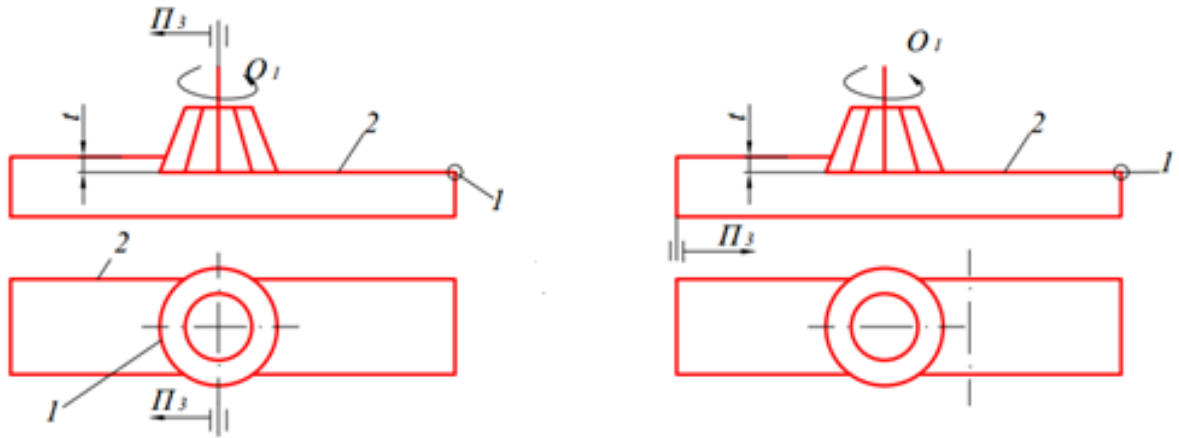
Фрезерування площини за допомогою торцевої фрези
